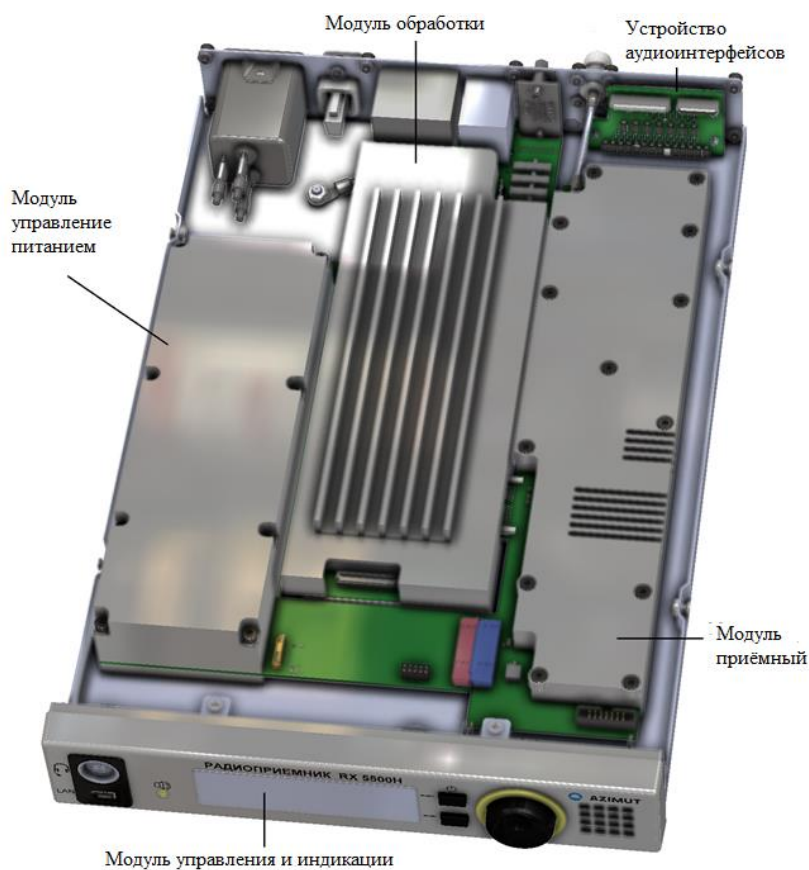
Внутренняя компоновка модулей в корпусе изделия со снятой крышкой
